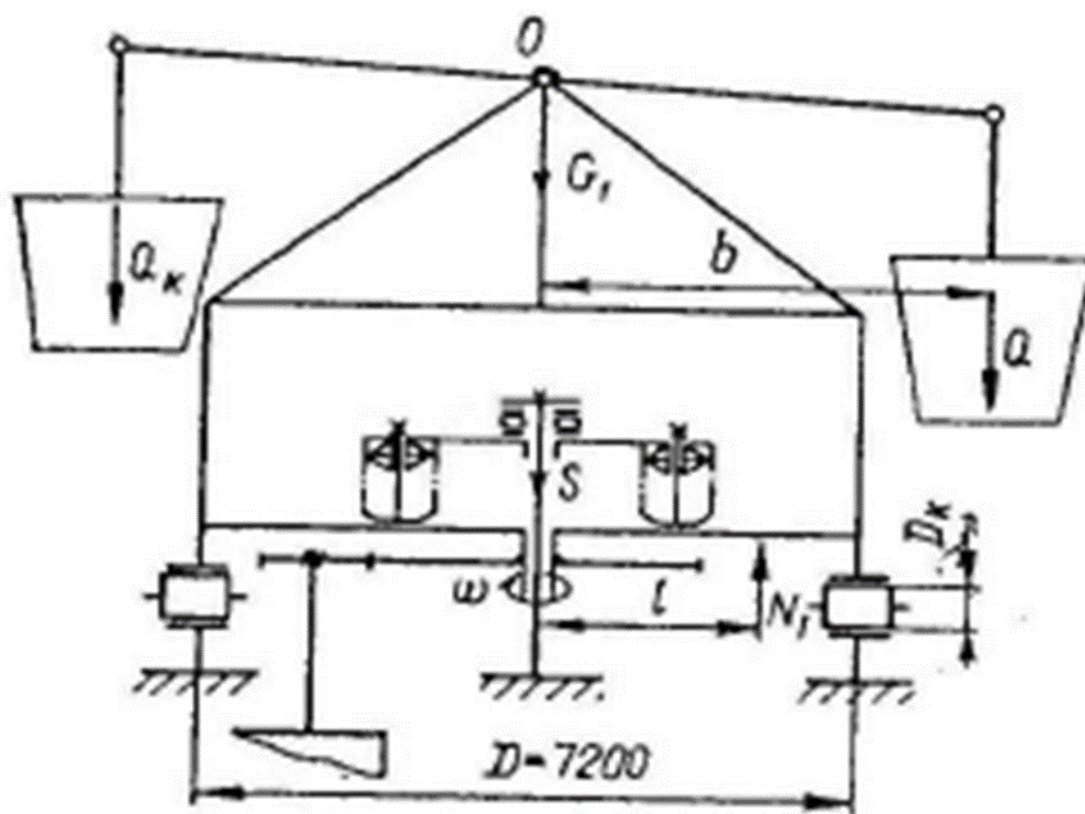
Схема механизма вертикального перемещения ковшей поворотного сталеразливочного стенда
